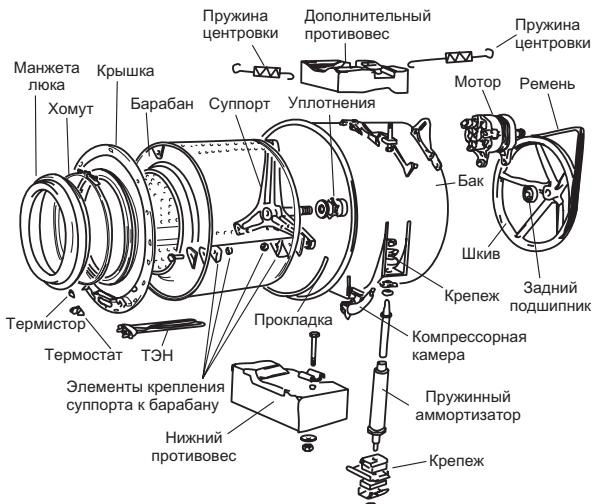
Компоновка СМА с двумя пружинно-поршневыми амортизаторами
